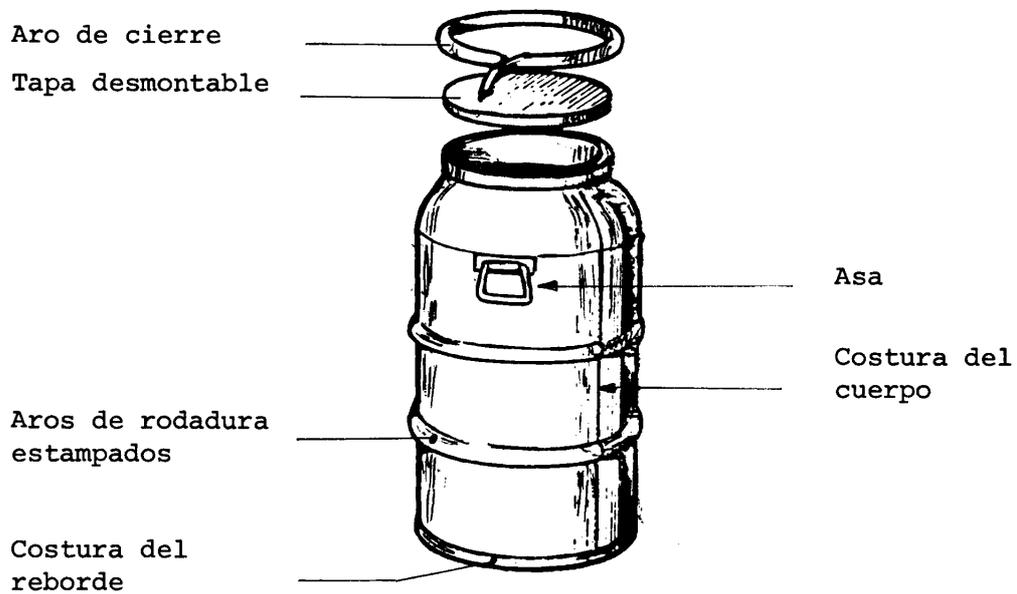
Tambor de acero o de aluminio de tapa desmontable
